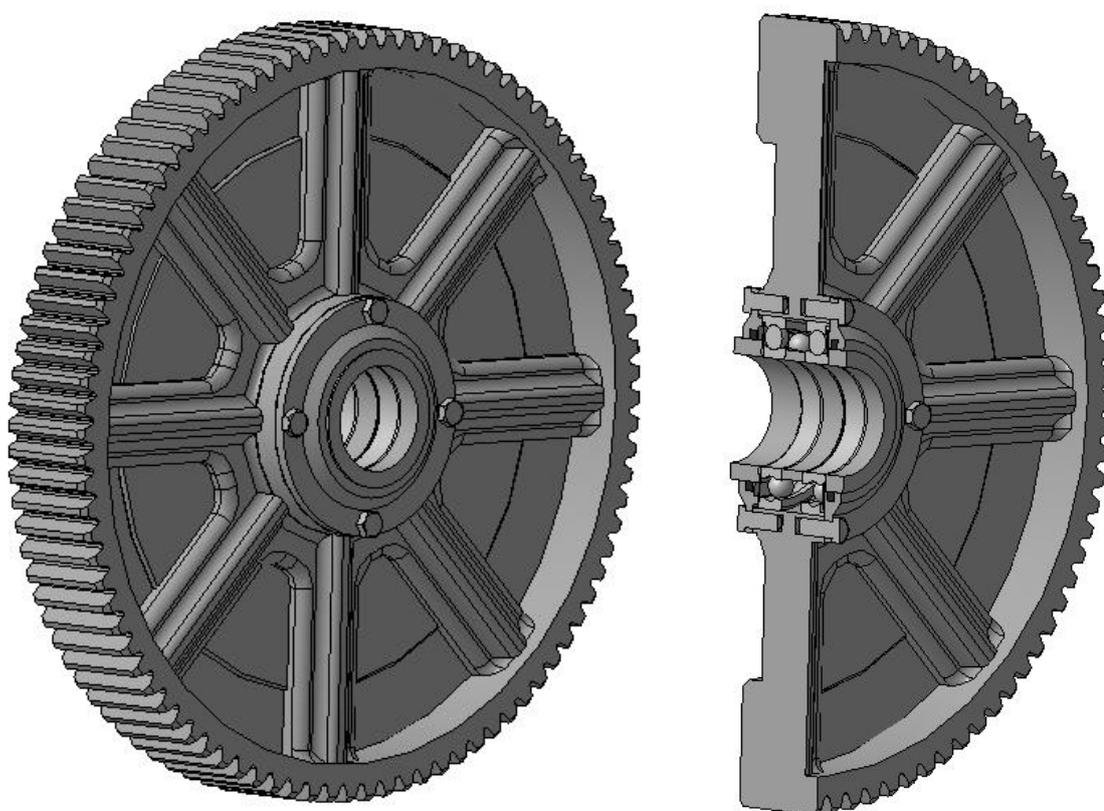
Сборочная 3D-модель узла пресса «Колесо зубчатое»
